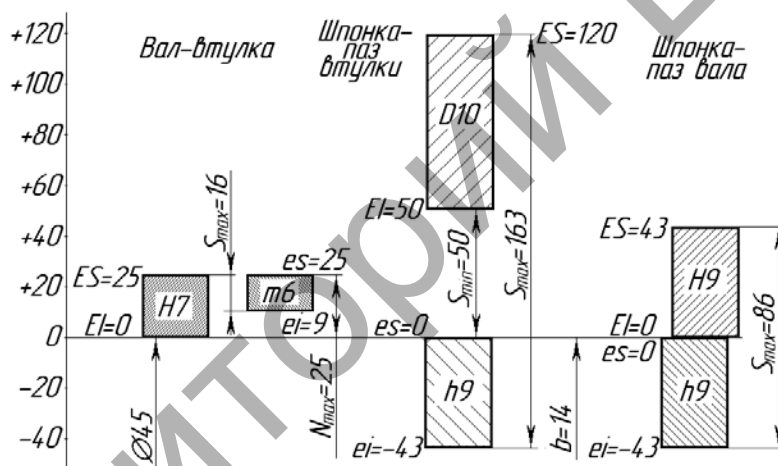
Схема расположения полей допусков шпоночного соединения
